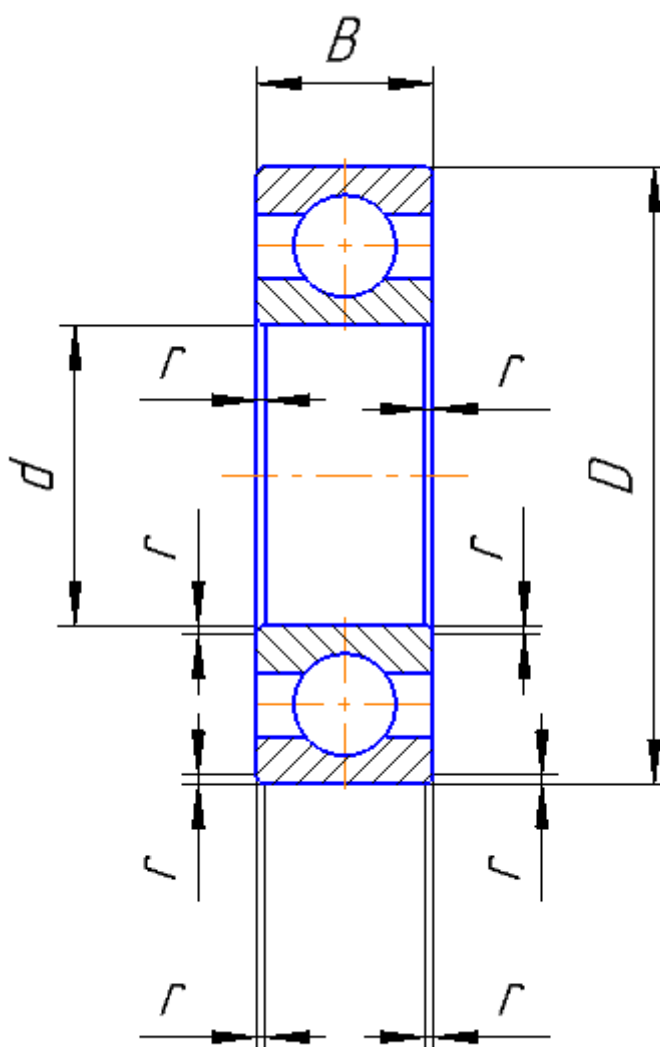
Подшипник качения радиальный шариковый.
